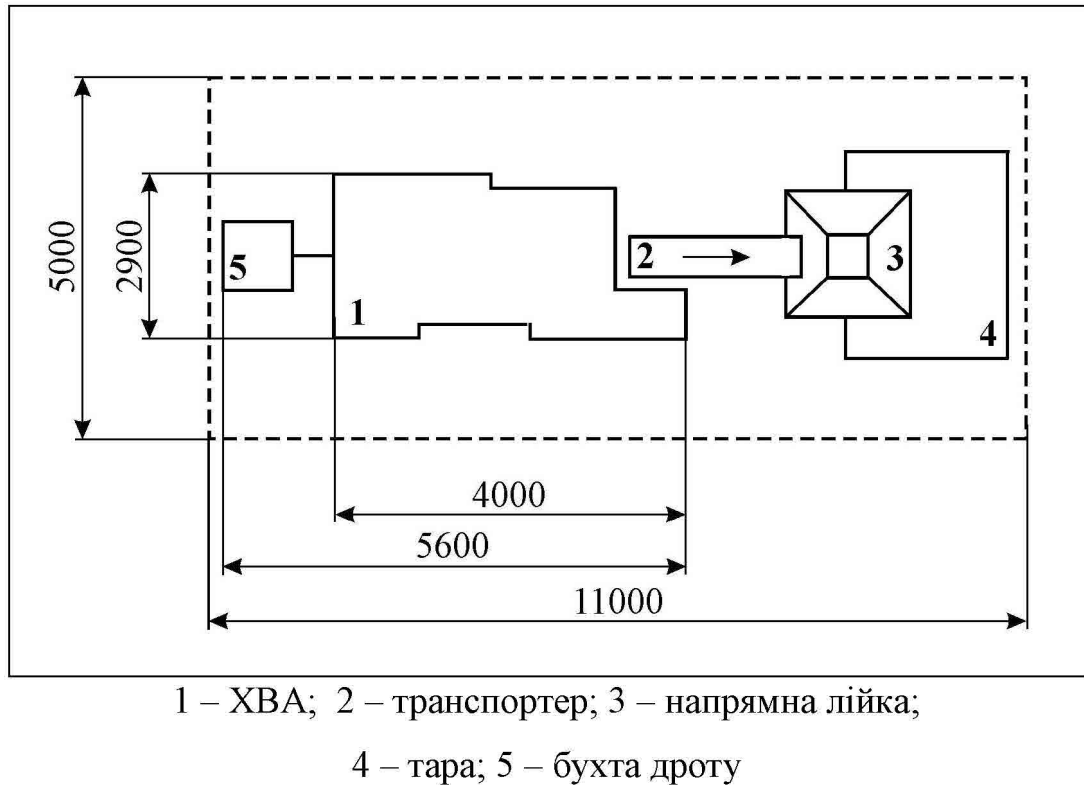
Схема організації робочого місця оператора ХВА типу А1920 для виготовлення деталі «Болт М10×30»
